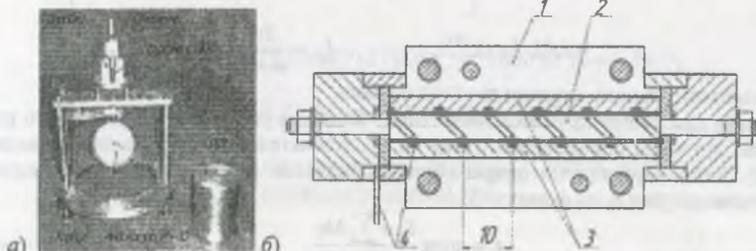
Устройство для испытания пружин (а); приспособление для навивки пружин (б)
